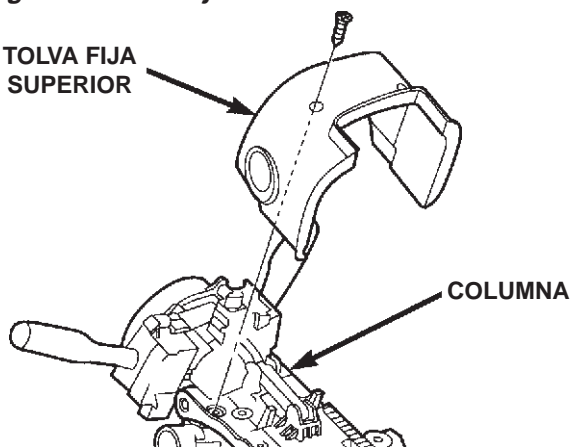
Desmontaje e instalación de la tolva fija de la columna
